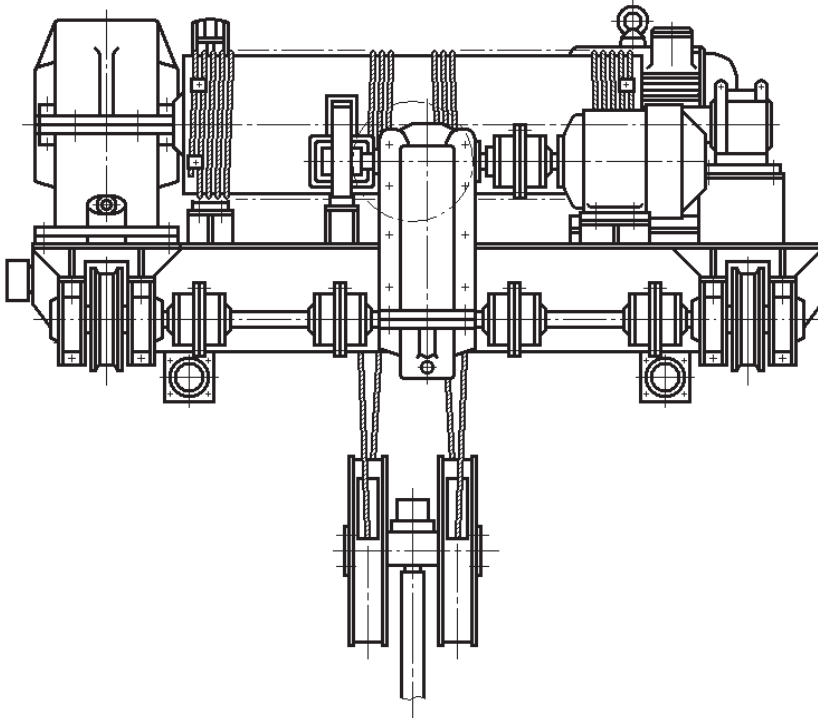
Механизм передвижения тележки с центральным расположением редуктора
